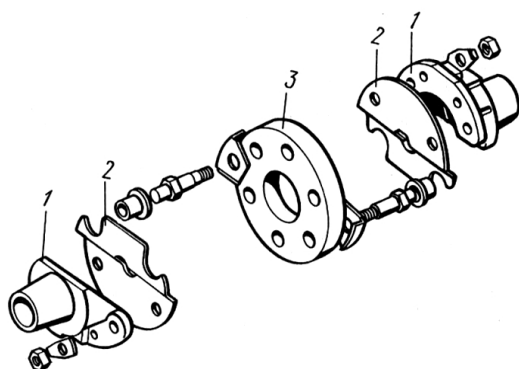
Травмобезопасный рулевой механизм с резиновой муфтой и предохранительными пластинами
